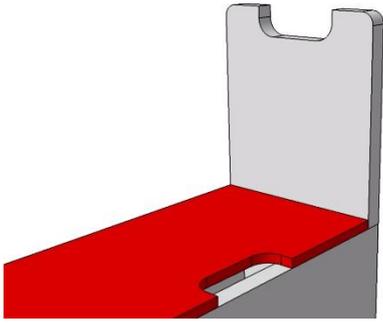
DETALLE TIRADOR CAJÓN PORTA JUGUETES I
